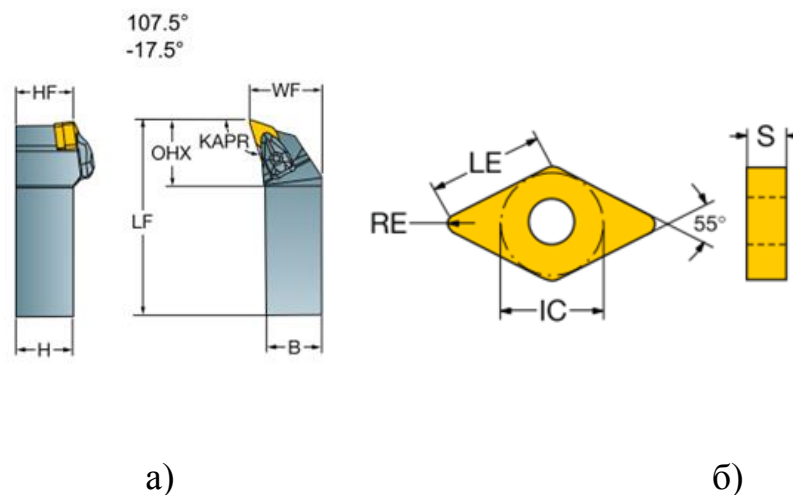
Инструмент для обработки поверхностей 2-5, 8-10, 12-15
